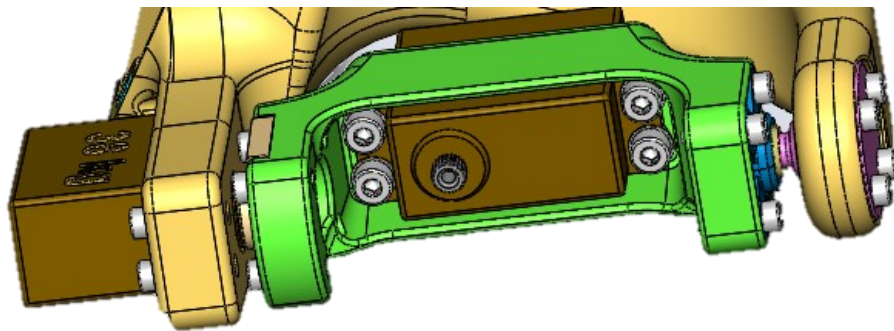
Čep pro zajištění kyvné funkce kloubu
